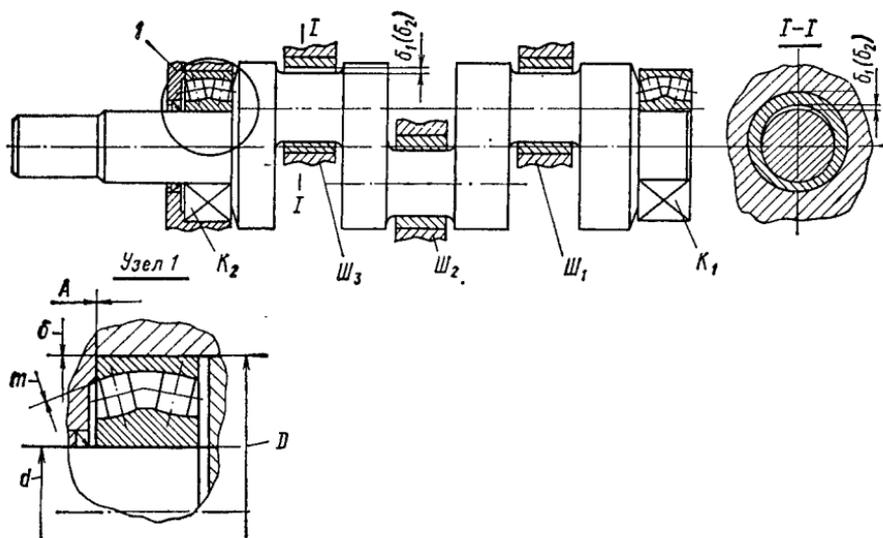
Формуляр контроля зазоров в подшипниках поршневого насоса:
